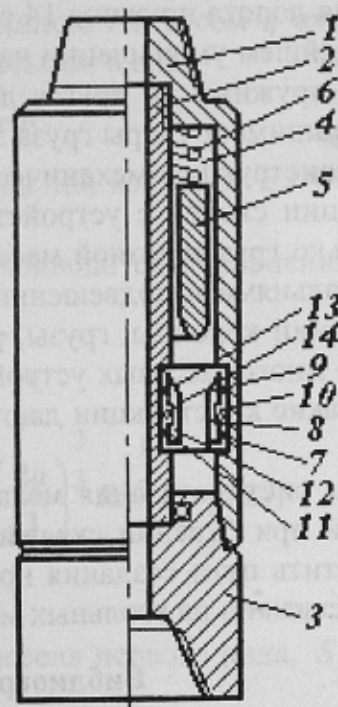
Устройство для создания ударной нагрузки на долото с выдвижными наковаль-нями: 1 – корпус; 2 – трубная вставка; 3 – на-ковальня; 4 – камера; 5 – груз; 6 – пружина; 7, 11 – кронштейны; 8, 12 – дополнительные наковальни; 9, 13 – ударные поверхности; 10, 14 – пружины
